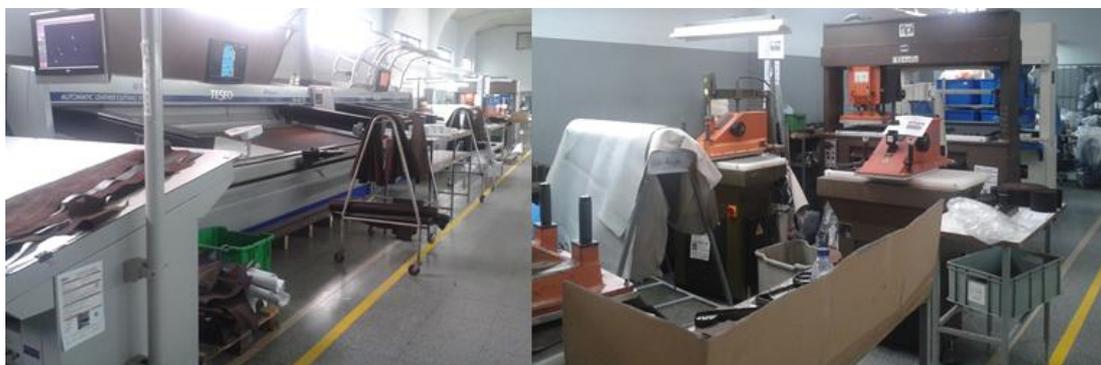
a) Secção do Corte automático da Armipex; b) Secção do Corte Manual da Armipex
